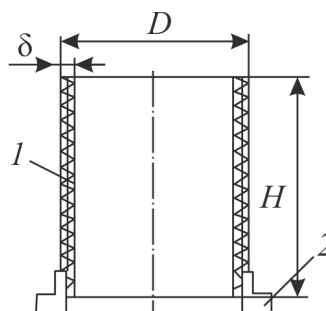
Конструкция нагревателя без паза: 1 – лапа; 2 – шина
